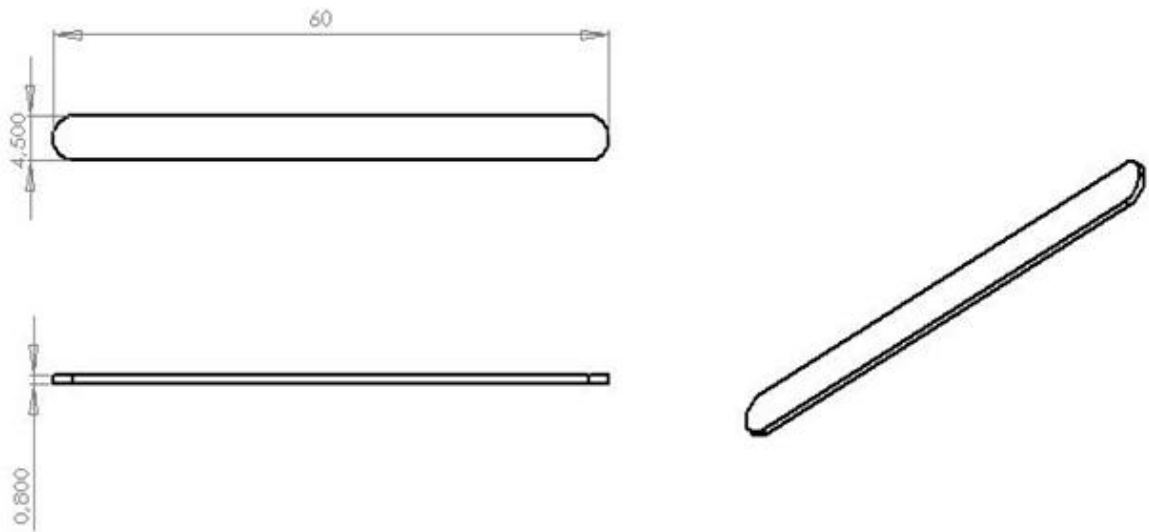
Representação esquemática bidimensional do inserto destinado a moldagem por sobreinjeção dos corpos de prova para ensaios dinâmicos-mecânicos.
